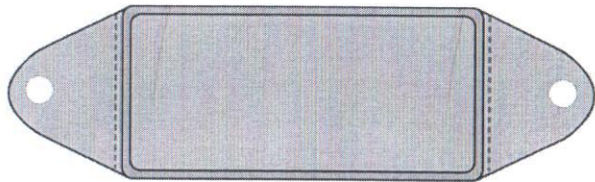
Контроль околошовной зоны сварного соединения коробки скользя с опорной плитой
